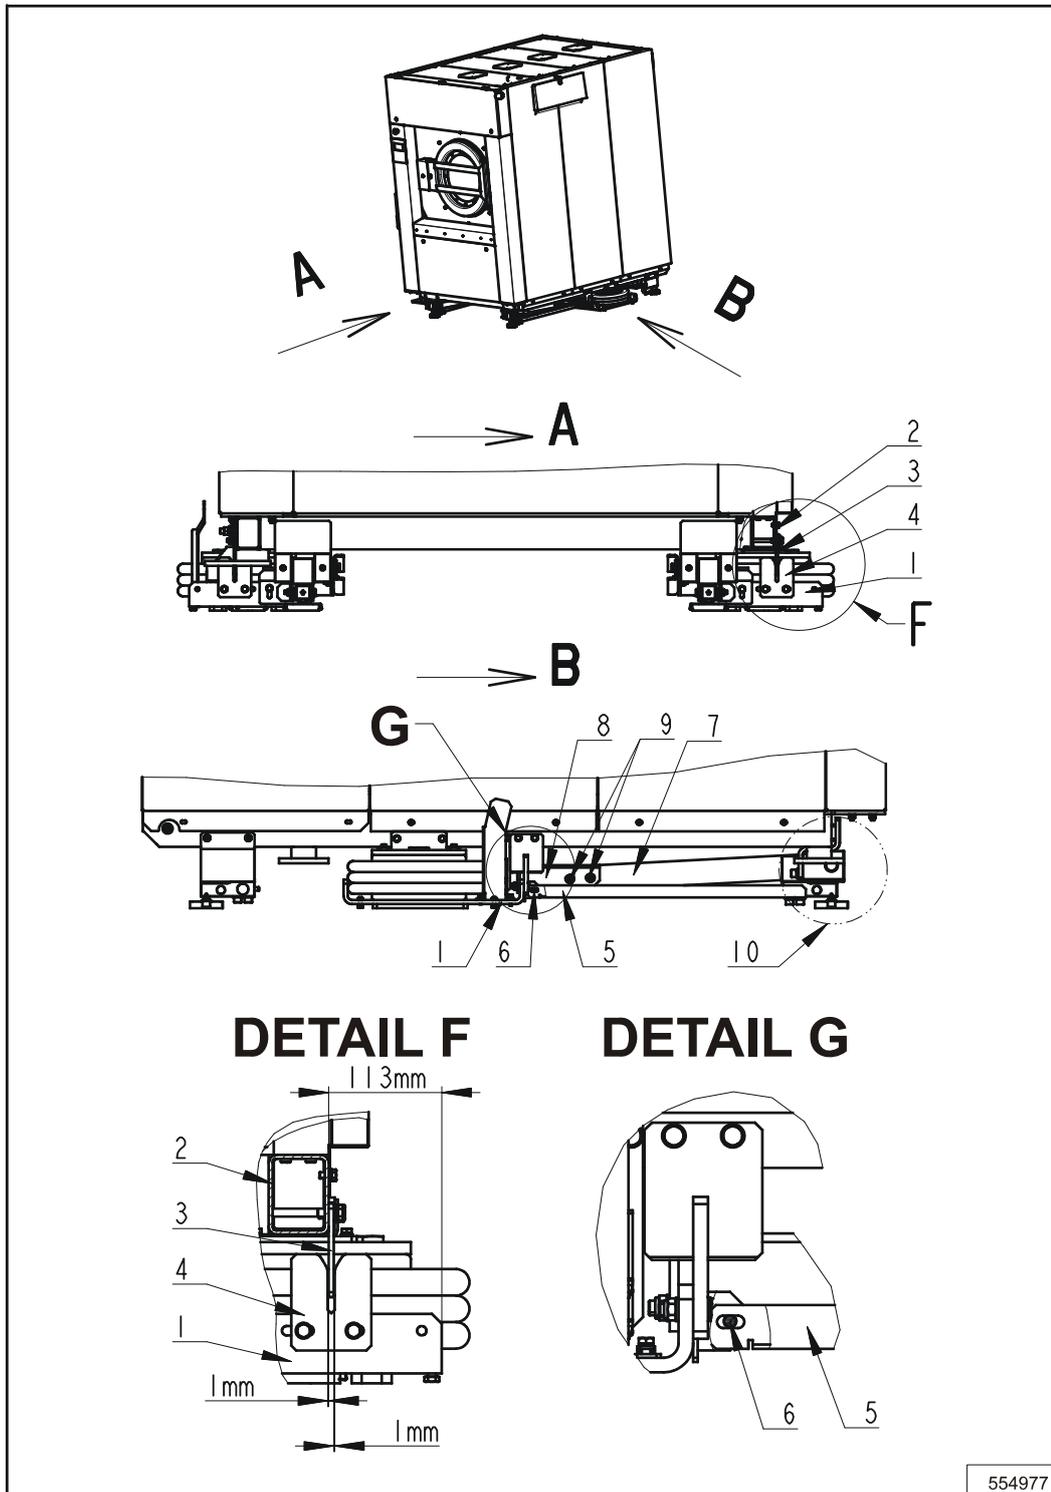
I. Máquinas 80-100-120 kg / 180-230-275 lbs con la inclinación delantera
